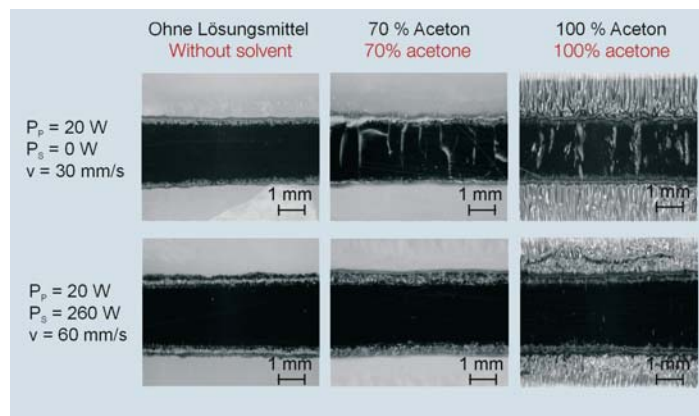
Nahtaufsicht von lösungsmittelbehandelten PC-Schweißproben; konventionelles Laserstrahlschweißen (obere Reihe) gegenüber hybridem Laserstrahlschweißen (untere Reihe)
